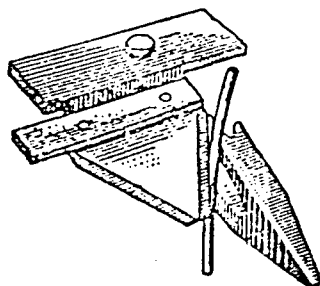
Suporte da planta no corte com a barra de corte. [31]
